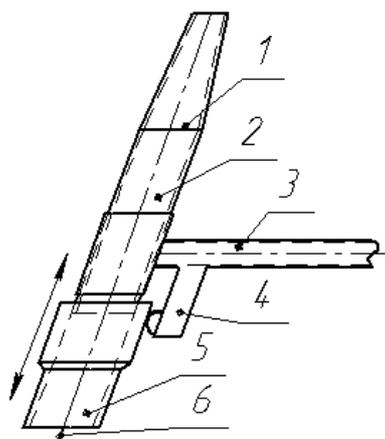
Схема горелки для аргонодуговой сварки
